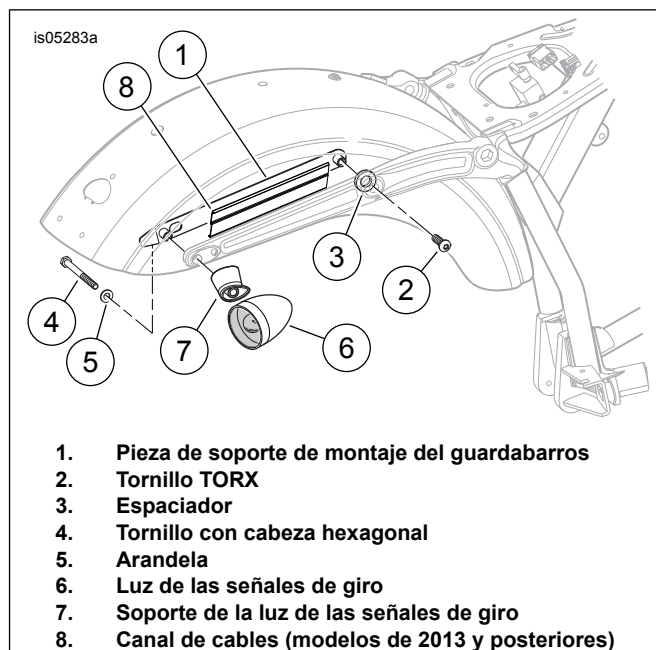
Extracción de la luz de las señales de giro del guardabarros
